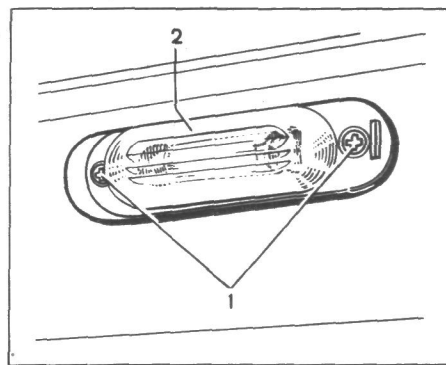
Фонарь освещения номерного знака: 1 — винты крепления; 2 — рассеиватель
